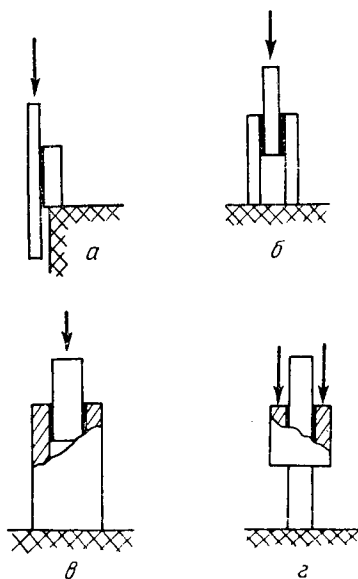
Схемы испытаний клеевых соединений на сдвиг при сжимающей нагрузке:
